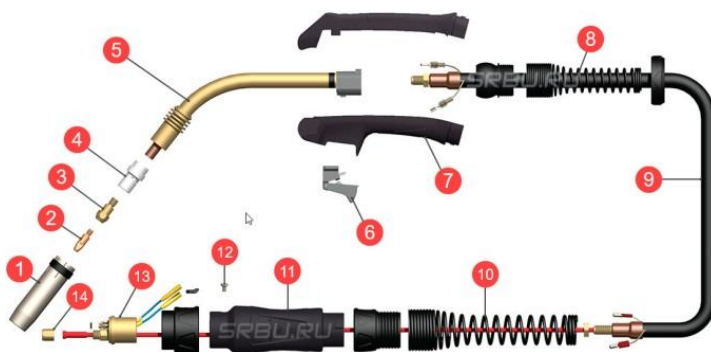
Конструкция горелки для сварки плавящимся электродом в защитных газах: 1 – сопло коническое; 2 – токовый наконечник; 3 – держатель наконечника; 4 – распределитель газа; 5 – мундштук; 6 – кнопка; 7 – рукоятка; 8 – соединительная пружина; 9 – коаксиальный кабель; 10 – соединительная пружина; 11 – коробка для охлаждения воздуха; 12 – винт; 13 – центральный коллектор; 14 – гайка
